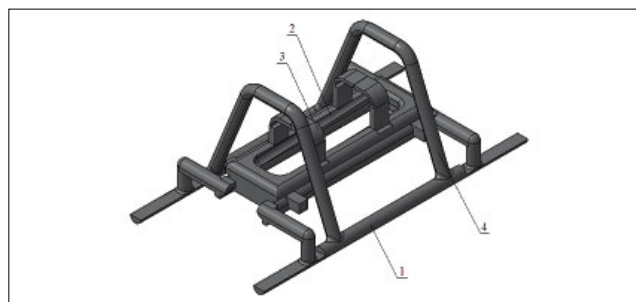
Крепление резервуара с БПЛА: 1 – опорные стойки; 2 – форма под емкость; 3 – раздвижные фиксаторы емкости; 4 – ножки для БПЛА
